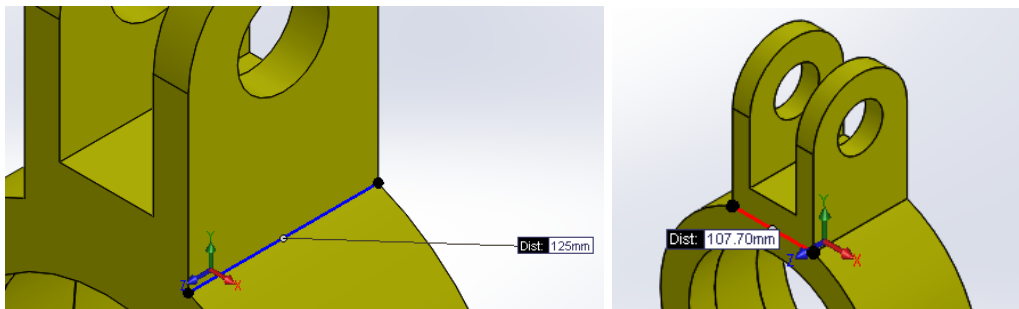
Línea del cordón de soldadura del elemento 3
